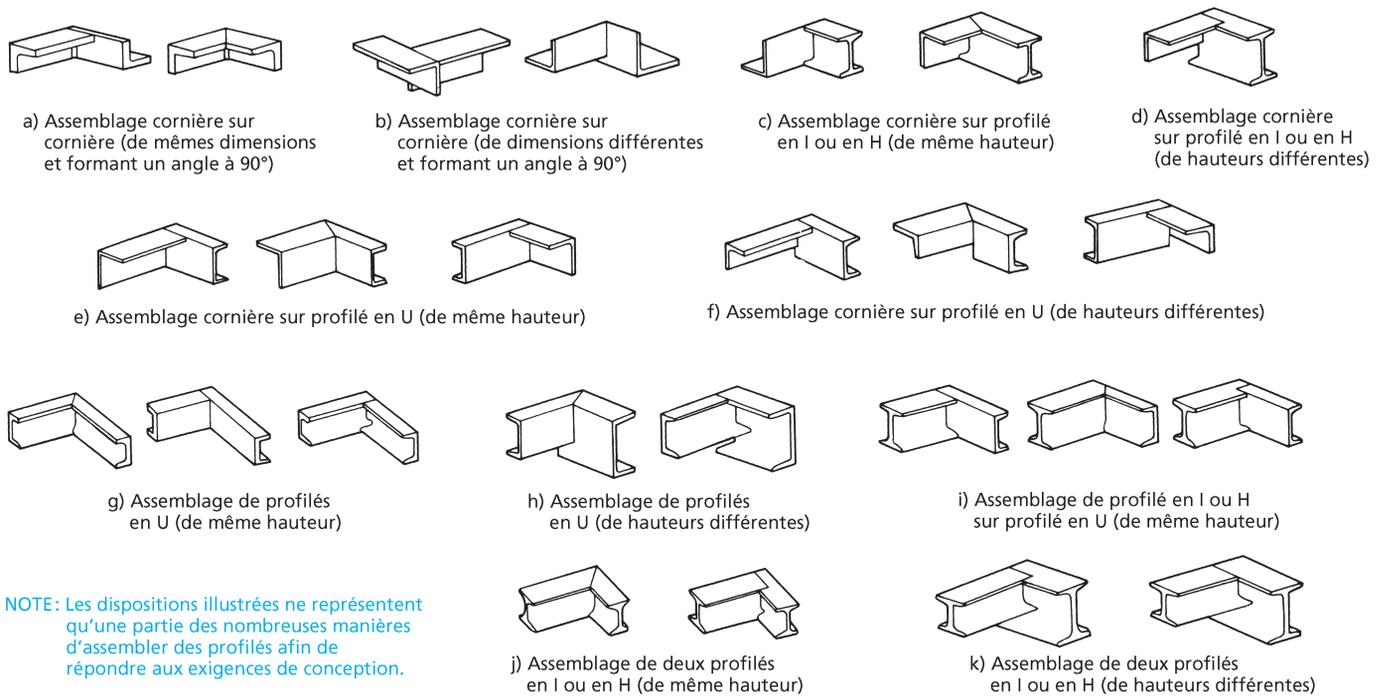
■ Assemblage de profilés identiques ou dissemblables.
